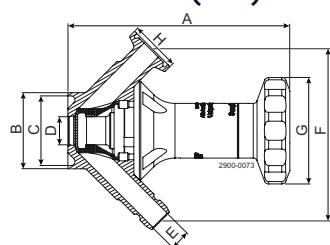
Manilla con cuerpo de la válvula: Tubería anillada para soldar
